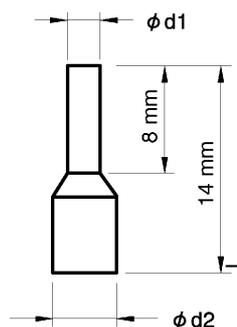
Dimensiones para terminales rectos sin soldadura
